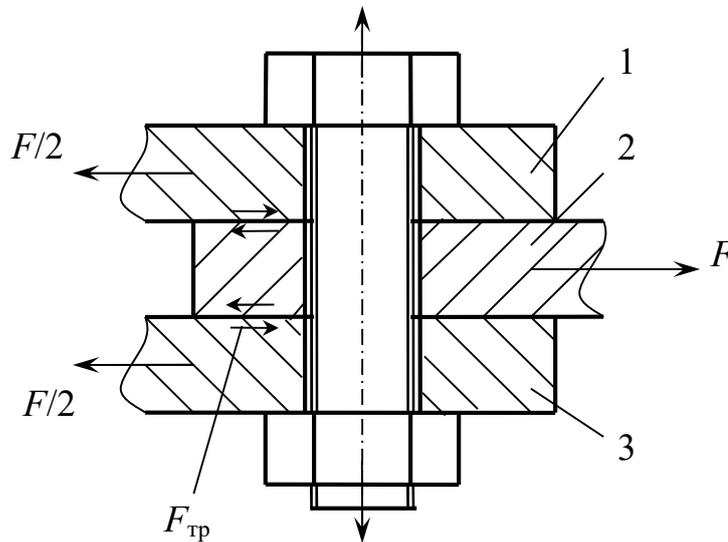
Соединение, нагруженное поперечными силами (болт в отверстиях с зазором)
